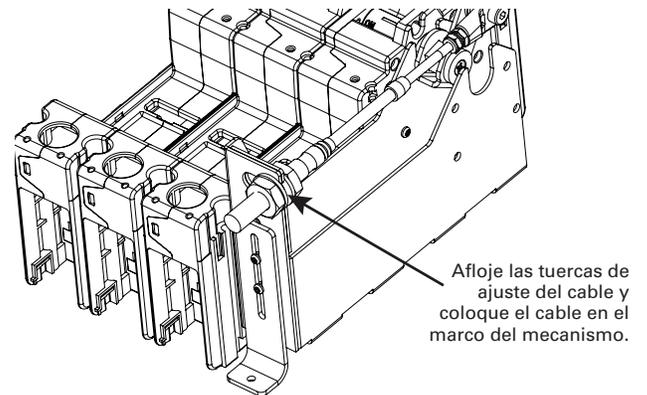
Instalar el cable en el marco del mecanismo.
